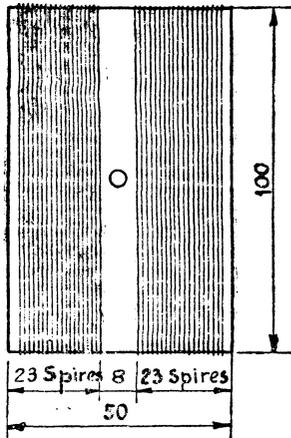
Type de bobinage sur un tube de 100 mm. de diamètre.
